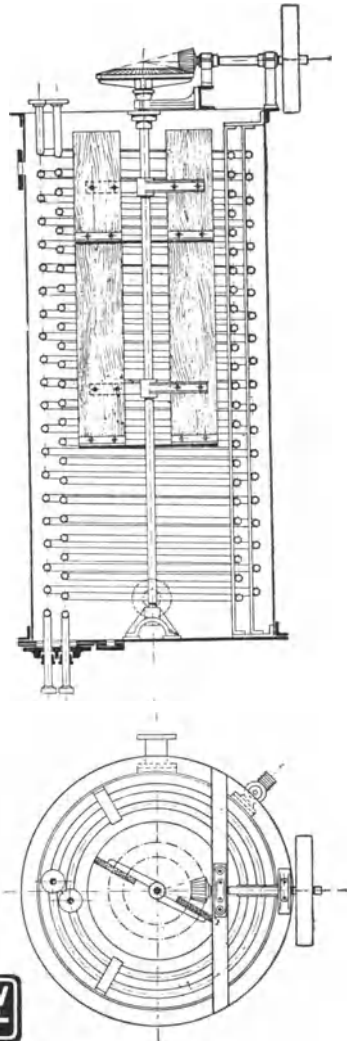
Offener Ammoniakverflüssiger mit Rührwerk. Gesellschaft für Lindes Eismaschinen AG., Wiesbaden.
